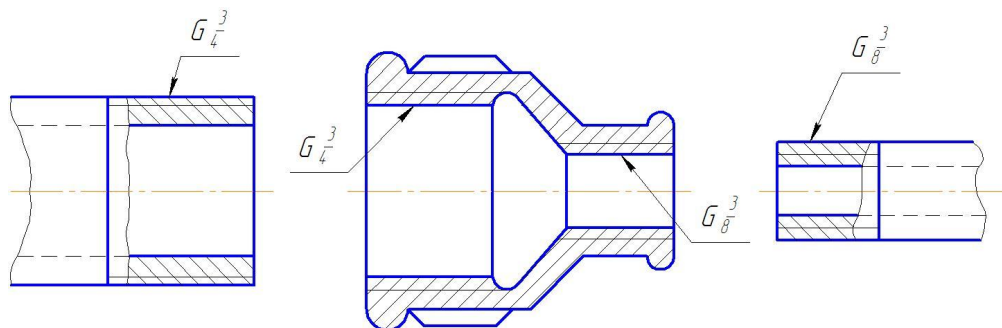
Обозначение размера трубной цилиндрической резьбы
